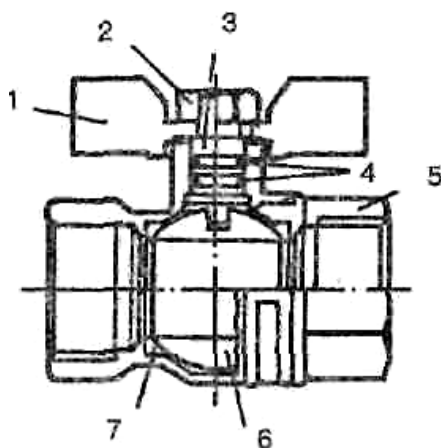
Шаровой кран: 1 - ручка; 2 - гайка, фиксирующая ручку на штоке; 3 - шток; 4 - уплотнительные кольца; 5 - корпус крана; 6 - шаровой затвор; 7 - уплотнительные тефлоновые кольца
